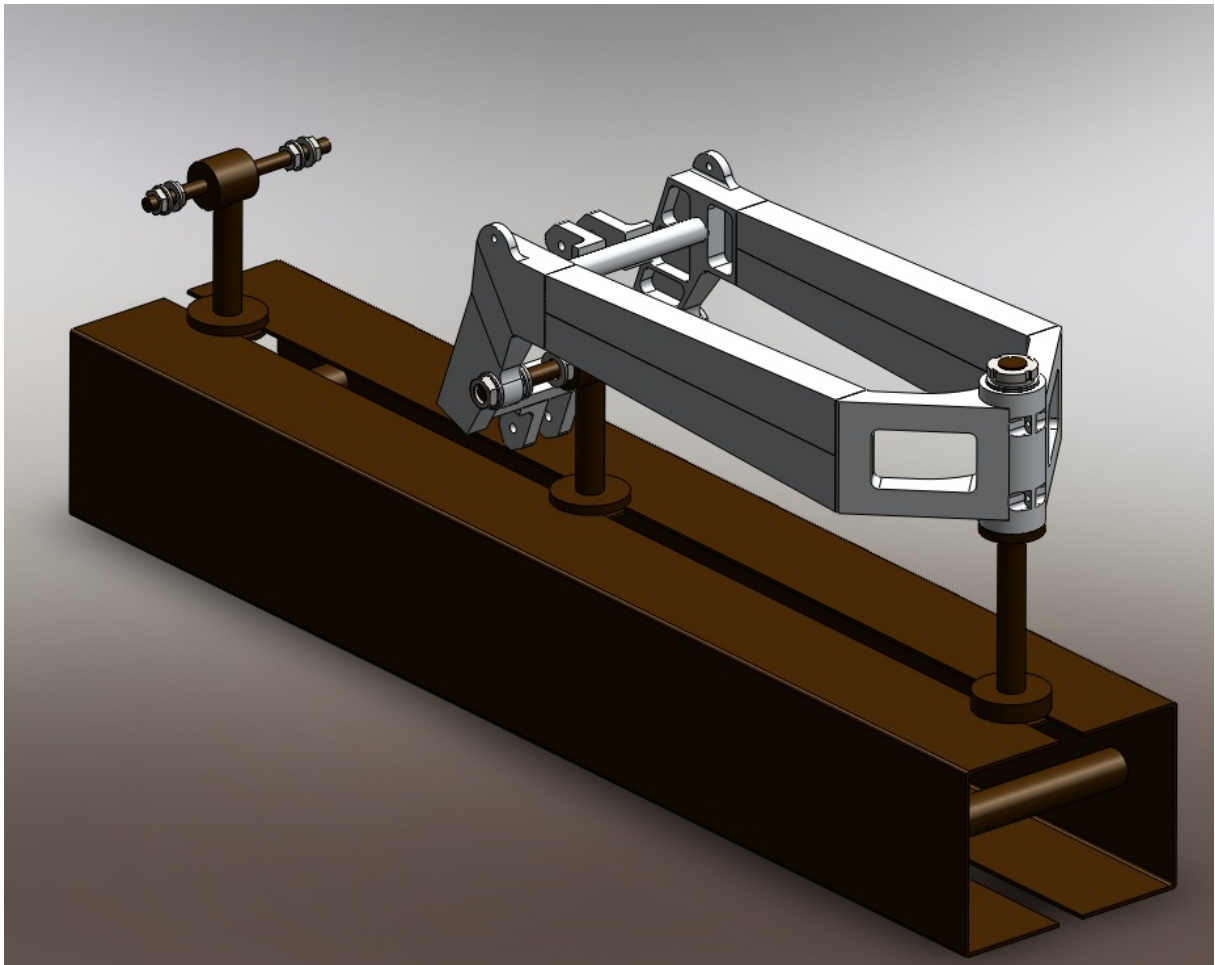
Chasis finalizado en el potro de soldadura
